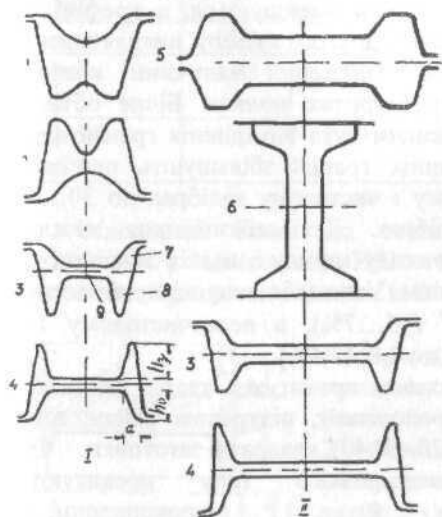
Типові схеми прокатки стандартних балок :
